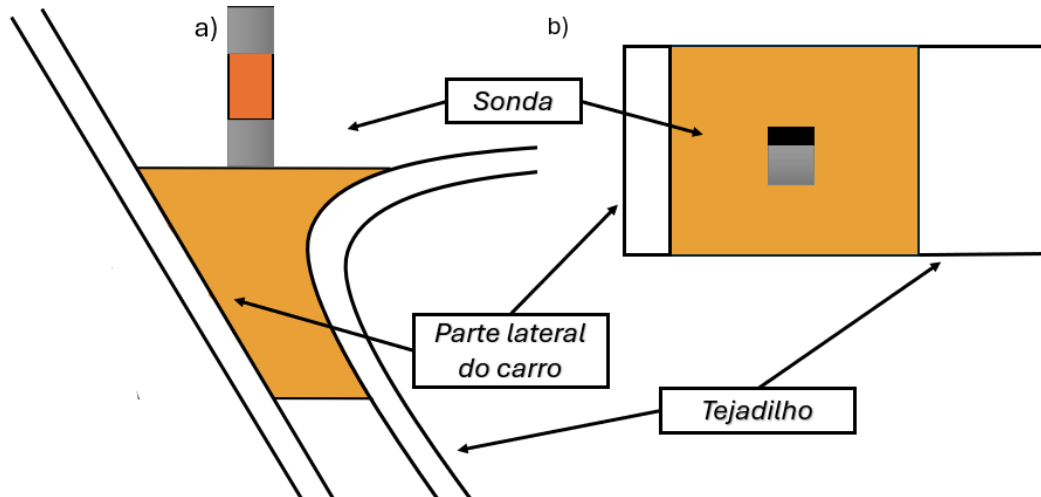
Posicionamento da bobina sob o cordão de soldadura durante o ensaio
